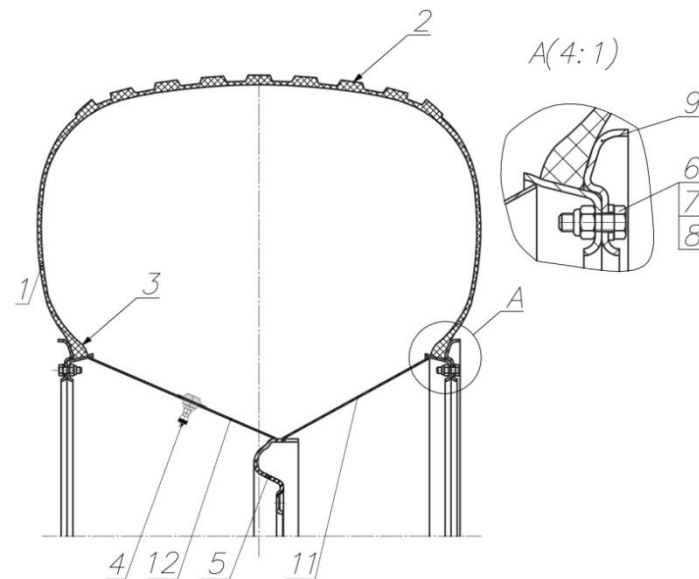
Шина 1300х600-533 ТРЭКОЛ с колесом в сборе
